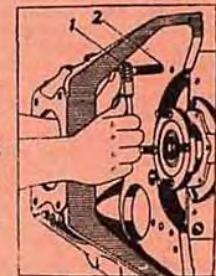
Если развертывать отверстия под установочные штифты в картере сцепления и блоке, как показано, можно добиться нужной точности:
